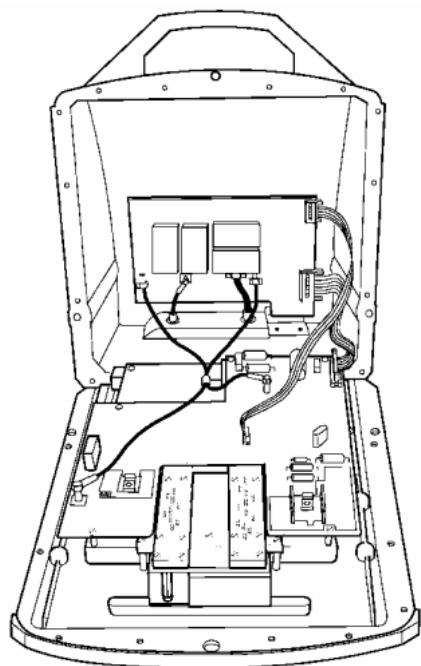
Внешний вид радиоблока *RAU1* с открытым корпусом
